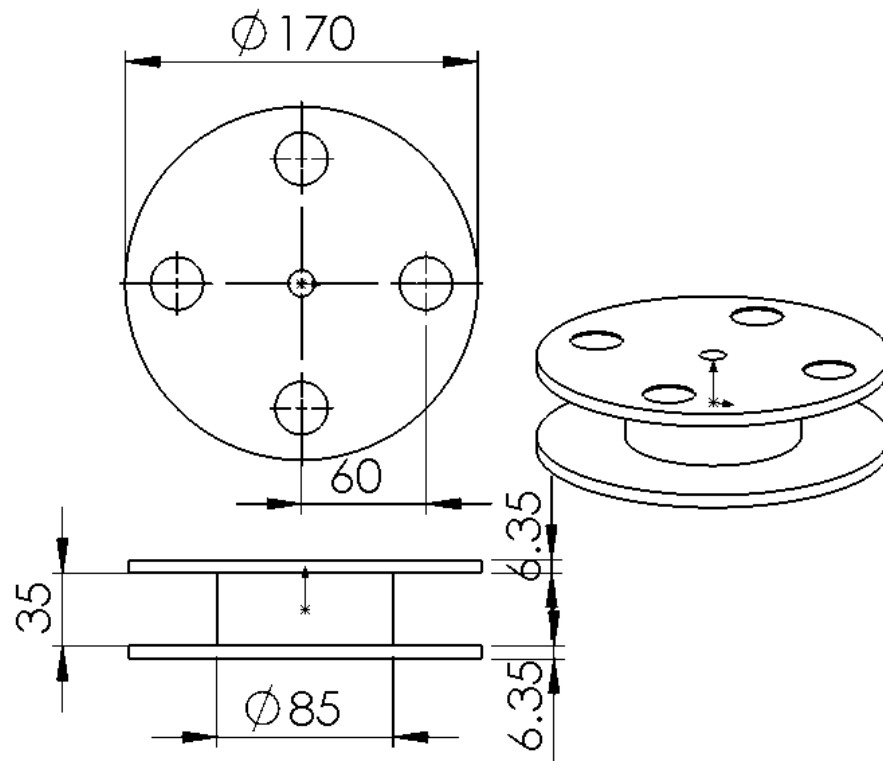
Dimensiones carrete inferior de acrílico de las bobinas Helmholtz.
